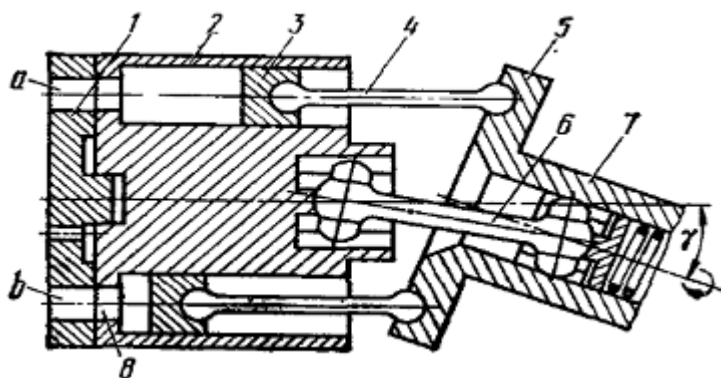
Схема аксиально-поршневого насоса: 1-крышка блока цилиндров; 2 блок цилиндров; 3-поршни; 4-шатуны; 5-регулирующий диск (шайба); 6-кардан; 7-ведущий вал; 8-отверстия.
